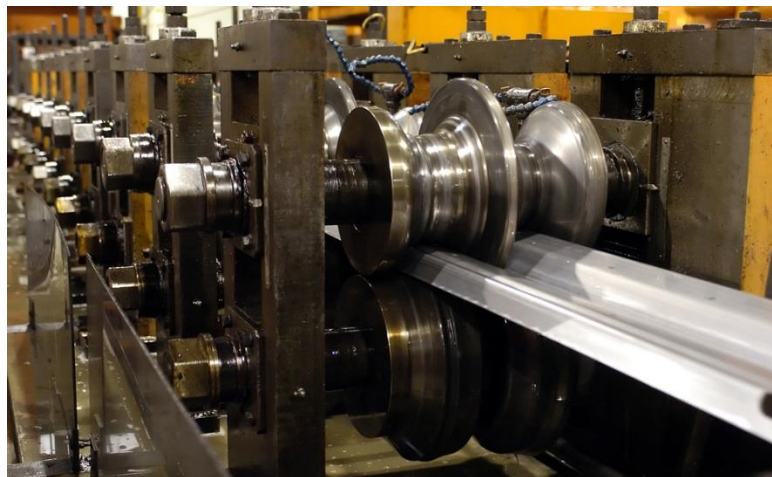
Máquina automática de laminagem a frio de perfis
